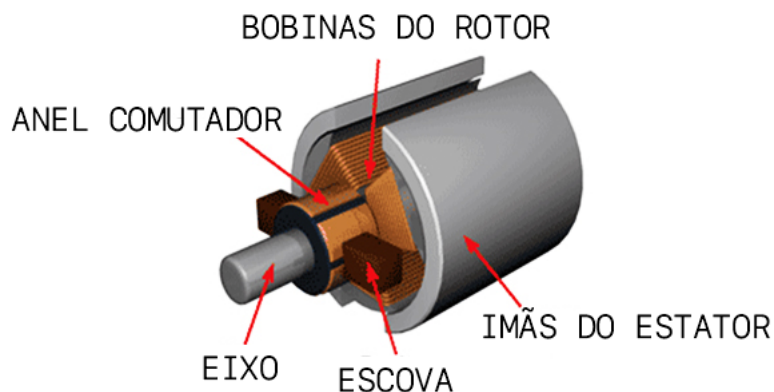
Parte interna de um Motor com Escova (Fonte: [18]).
